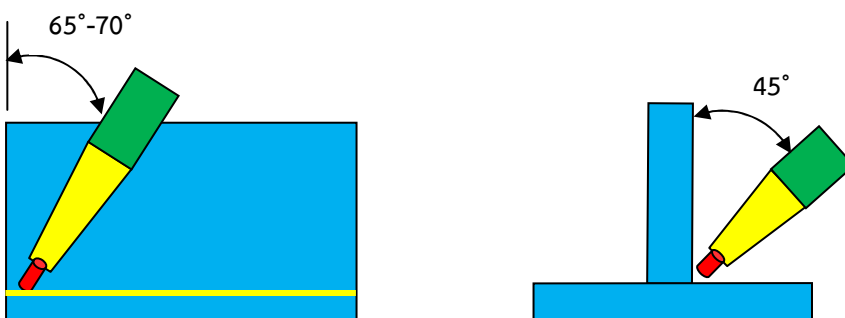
การเชื่อมท่าราบ (Flat Welding) 1F
